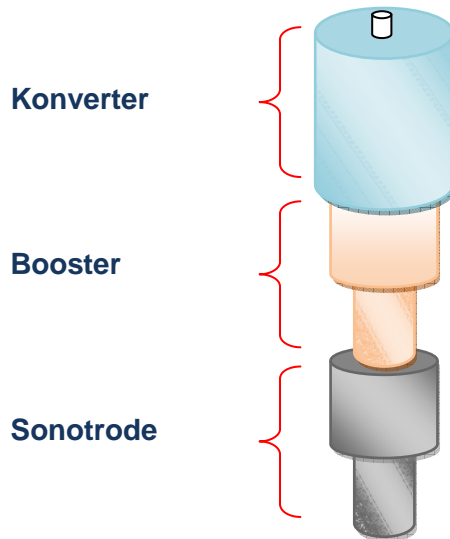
Prinzipsaufbau Schweißeinheit
